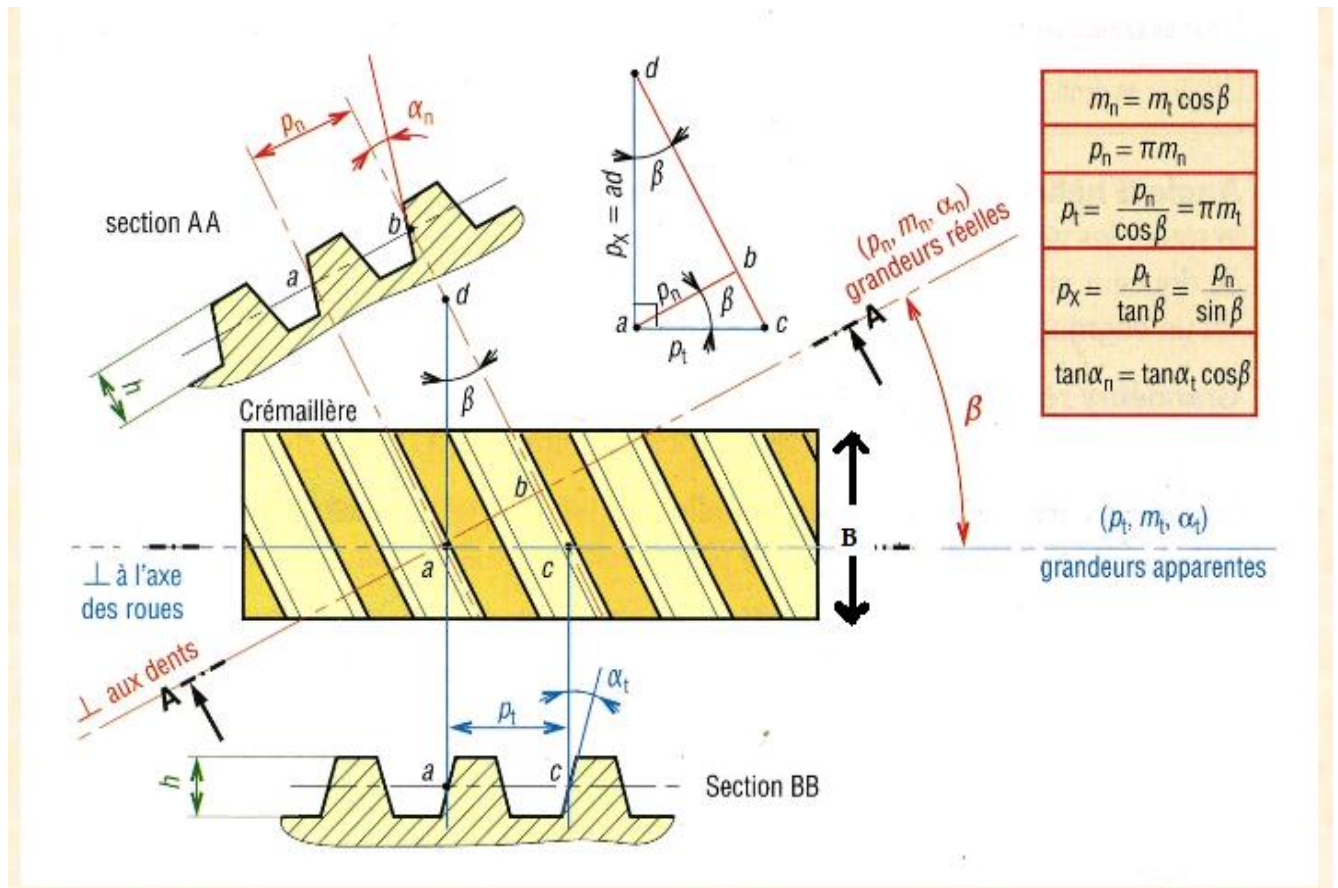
dessin illustratif de la largeur d'un engrenage
